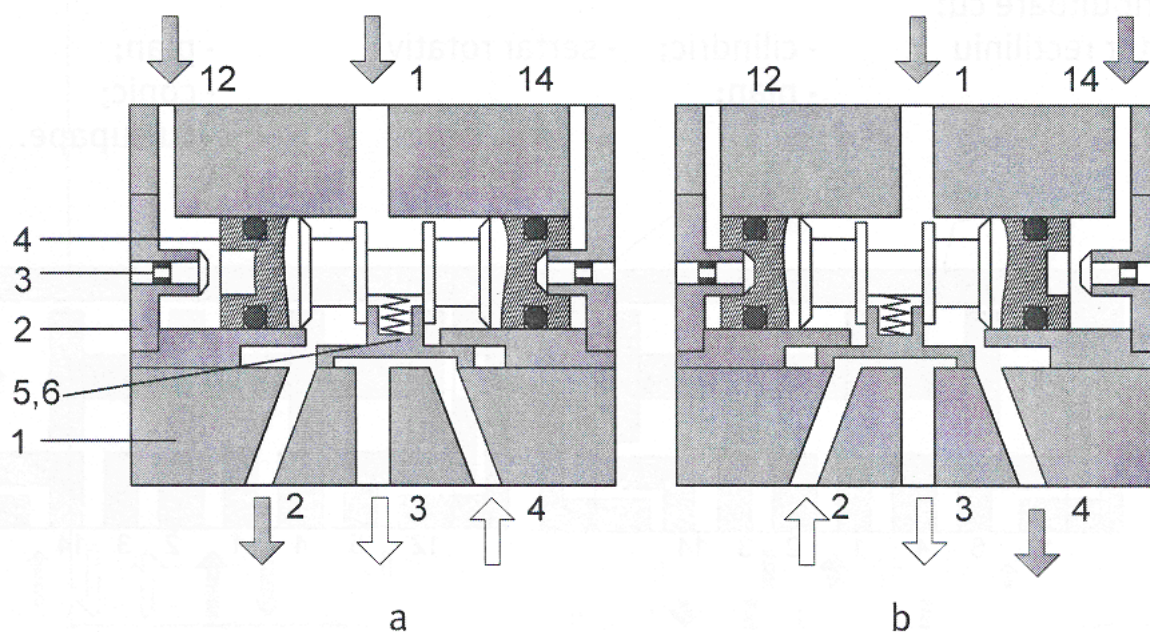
Distribuitor rectiliniu cu sertar plan 4/2: 1 – corp; 2- capace; 3 - elementele de comandă manuală; 4 – pilot; 5 - sertar plan.
